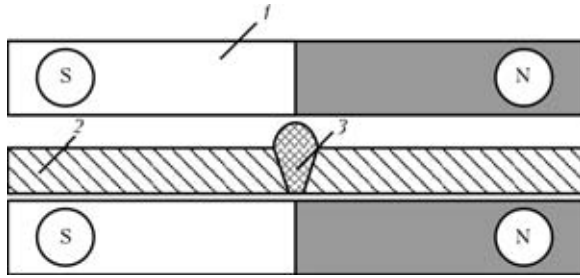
Схема экспонирования образца алюминиевого сплава наплавкой в неоднородном магнитном поле: 1 — магниты; 2 — образец; 3 — зона наплавки
